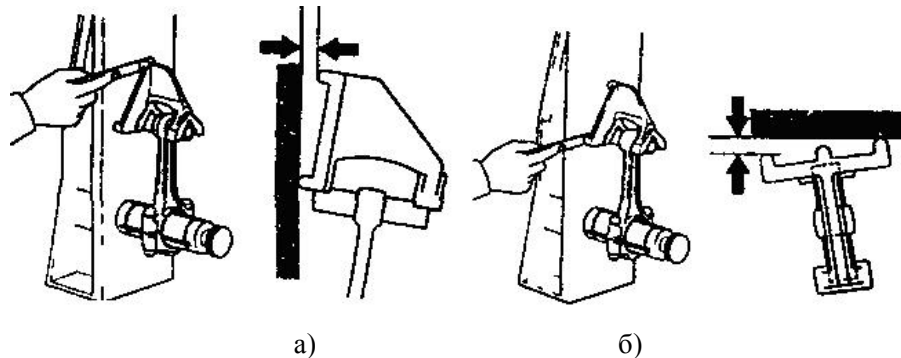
Приспособления для проверки шатуна на погнутость и скручивание: а) проверка на изгиб, б) проверка на скручивание.
